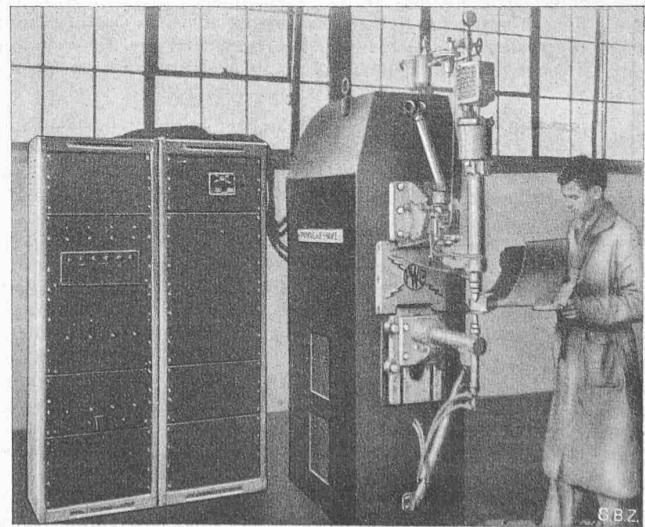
Progressive Welder-Punktschweissmaschine für Leichtmetalle
